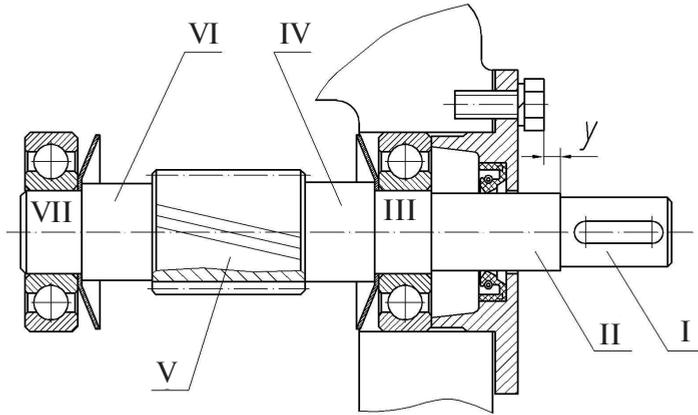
Эскизная компоновка быстроходного вала редуктора
